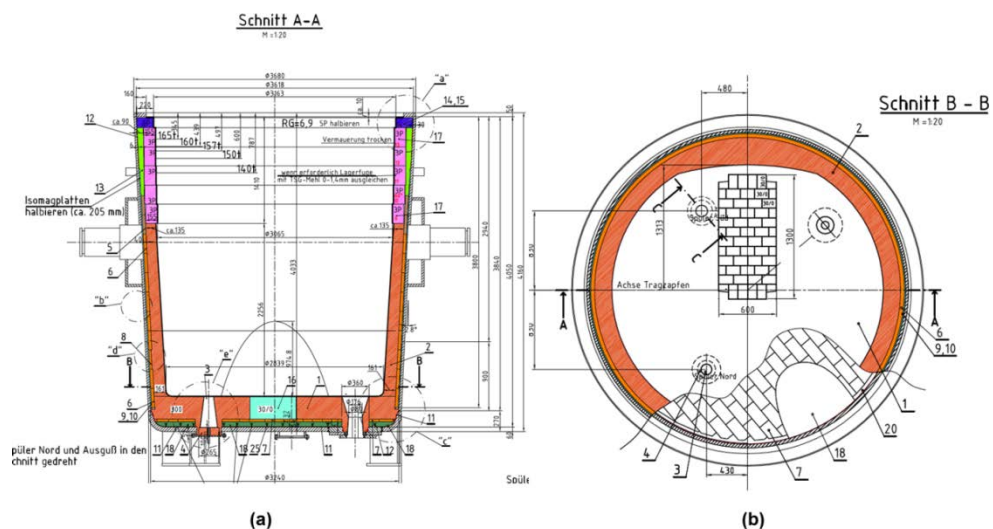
Konstruktionszeichnung der untersuchten Stahlpfanne; Querschnitt (a) Draufsicht (b)
